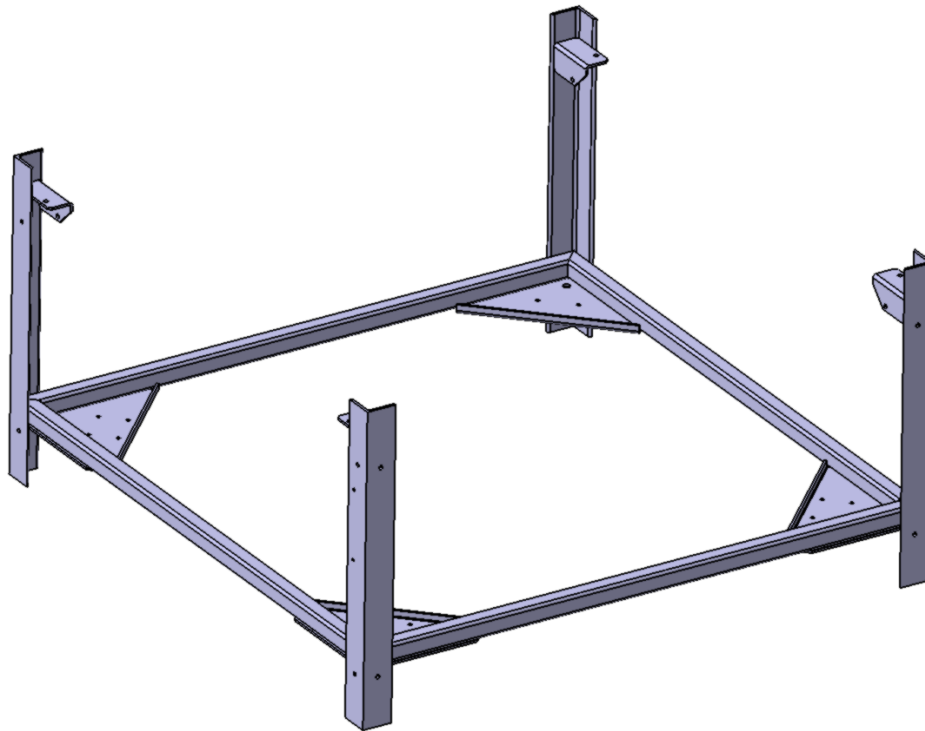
Soldadura ("TFG-21000"). Forma la estructura sobre la que se apoya el Conjunto superior [captura del diseño en Catia V5].
